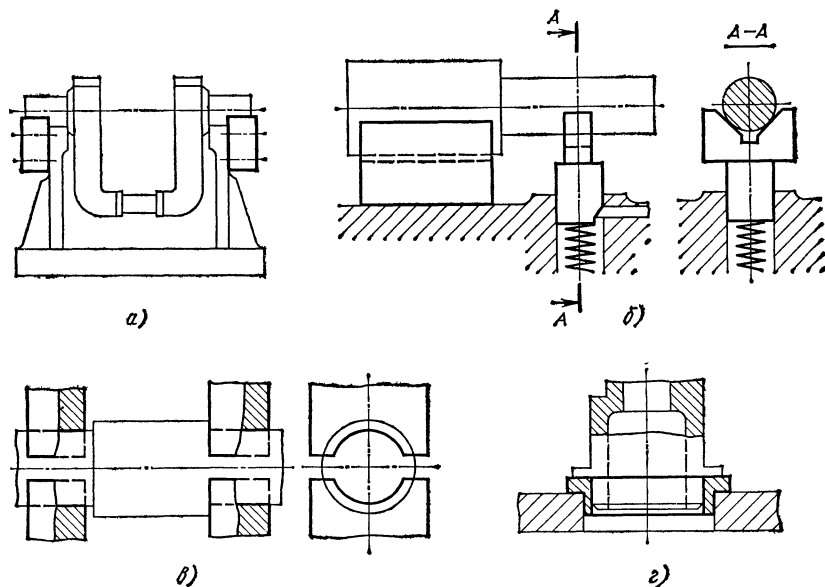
Примеры установки заготовок наружной цилиндрической поверхностью: а — коленчатого вала в две призмы; б — ступенчатого валика в призму с использованием самоустанавливающейся опоры; в — то же, в полуотверстия; г — во втулку (припаяют для заготовок с базой, выполненной по 6—8-му квалитетам)
